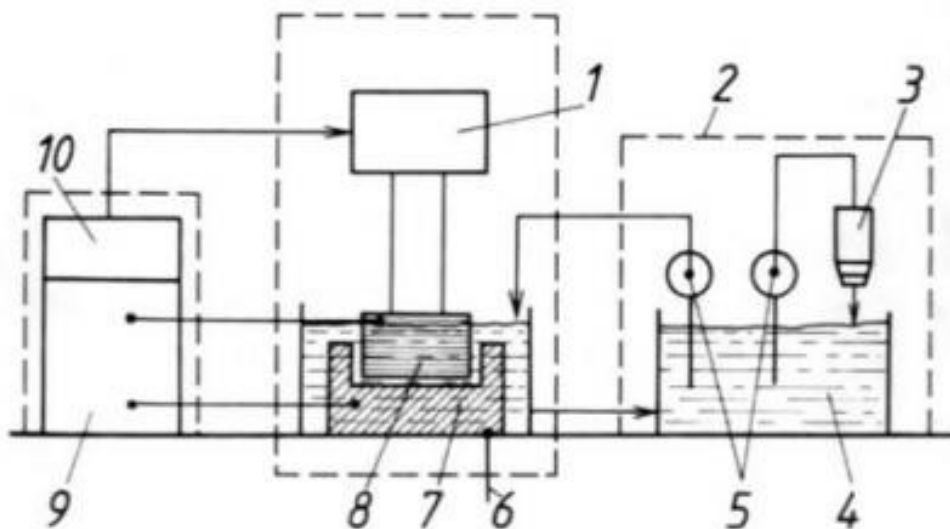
Princip výroby dutiny formy drátovou elektrodou [1]
